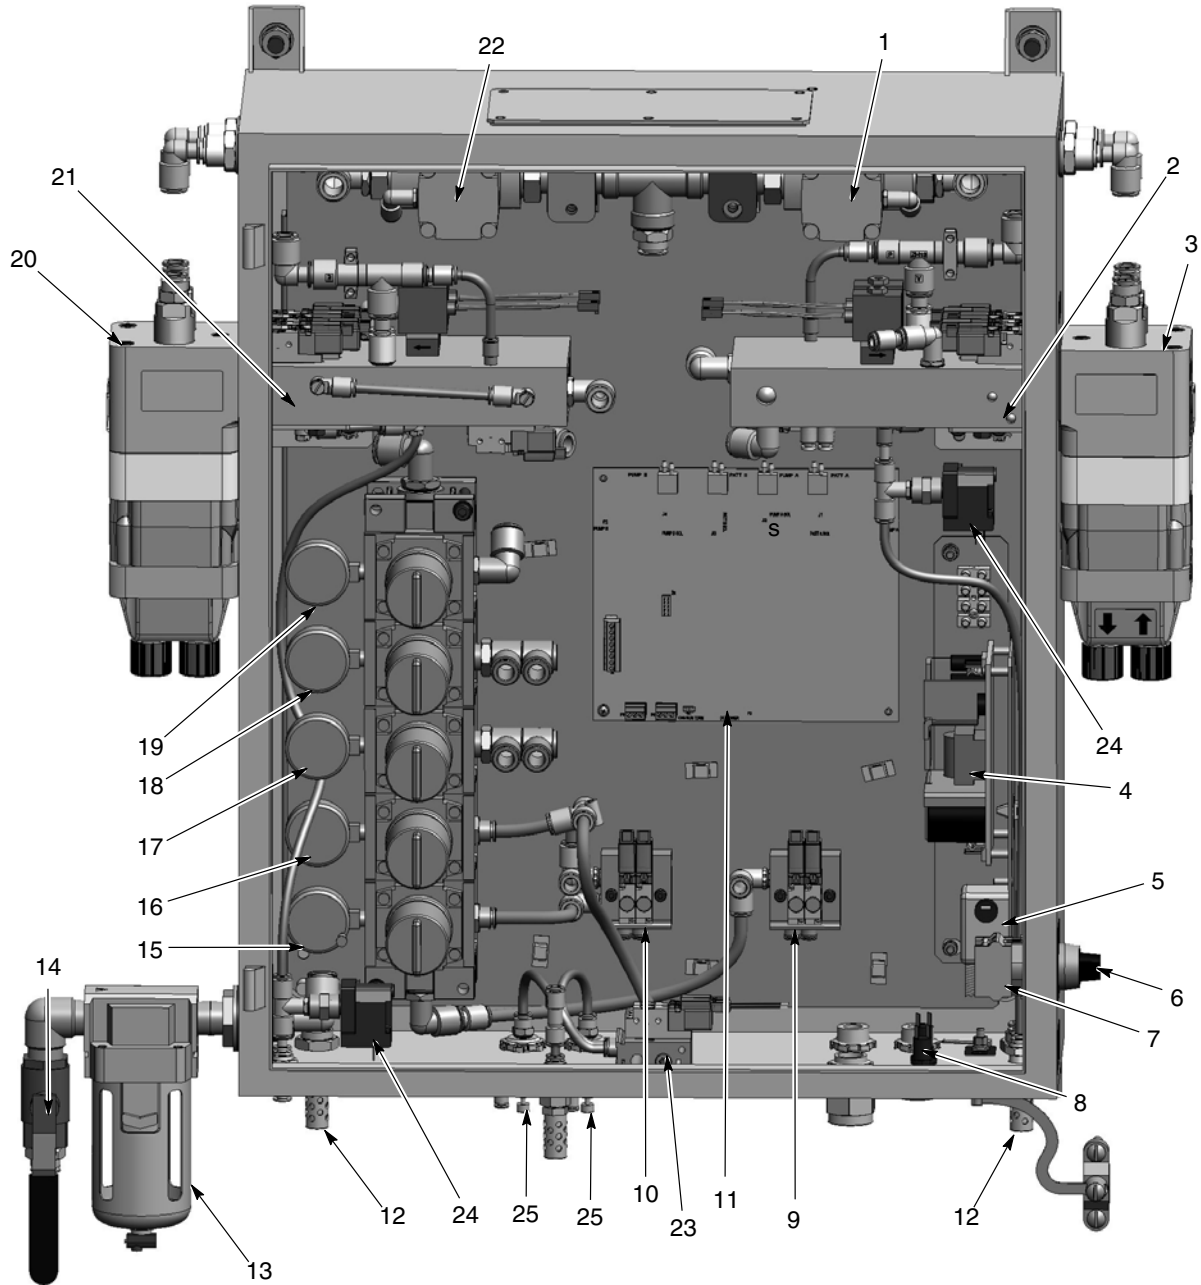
Komponenten des Pumpenschaltschranks (Abb.: System mit zwei Pumpen)
